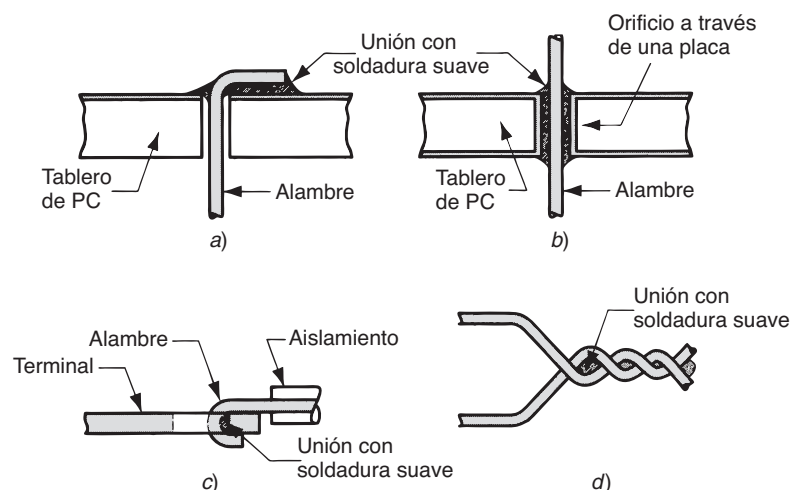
Técnicas para asegurar la unión con medios mecánicos antes de la soldadura suave en conexiones eléctricas:
